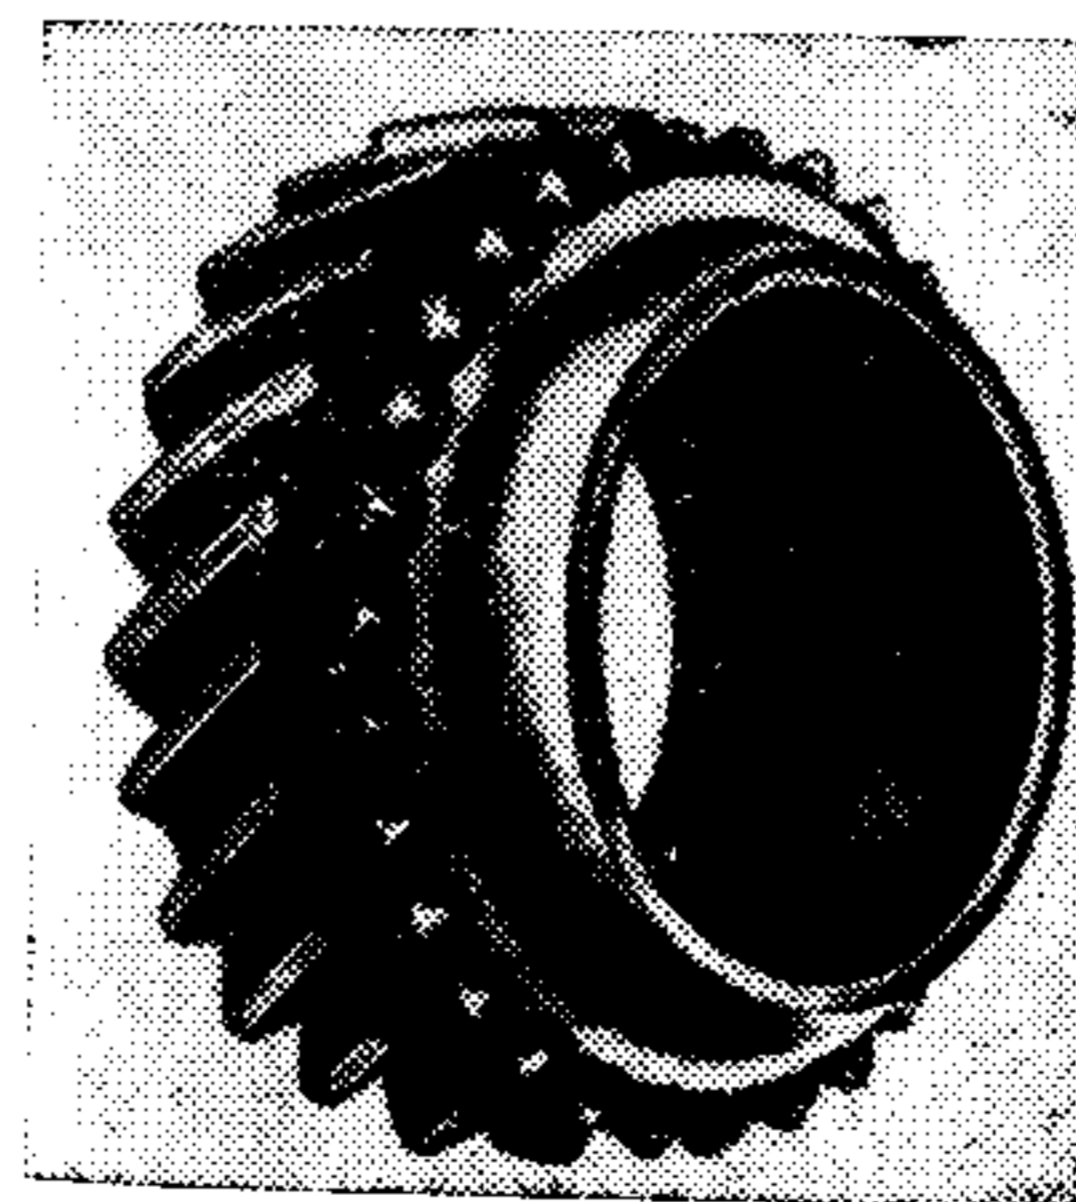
Зубчатый синхронизатор автомобильной коробки передач
